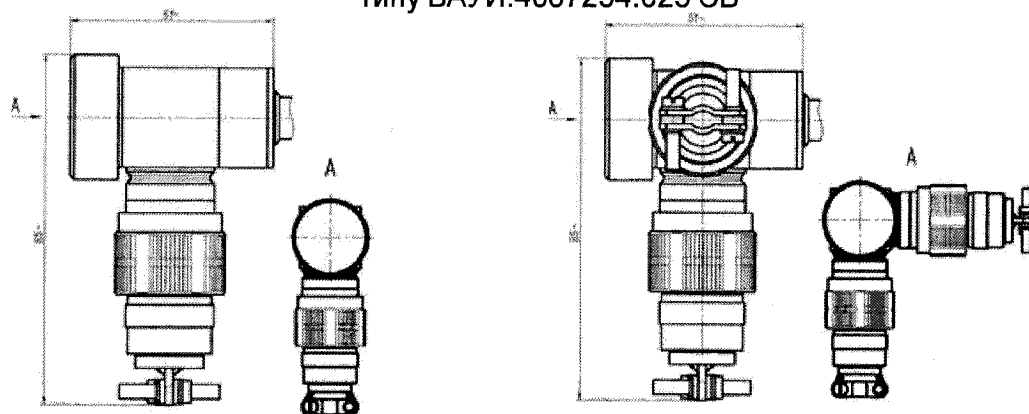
Кресленик зовнішньої частини ТСП-0690 (рис. 2) з головкою типу БАУИ.4087234.024 СБ
